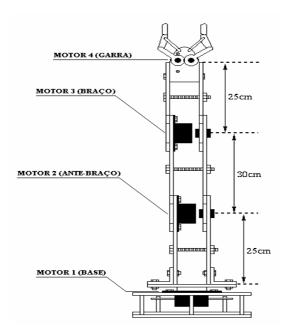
Vista Frontal do Robô Manipulador Rotatório
